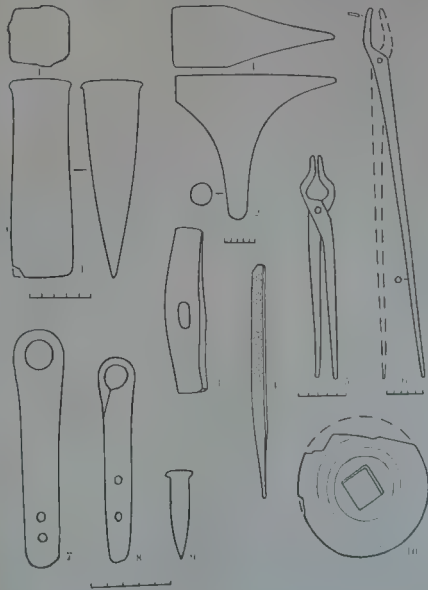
Инструменты кузнеца: 1 — наковальня из Витебска (Нижний замок); 2 — наковальня из Райковецкого городища (УССР); 3—5 — молоток, напильник и клещи из Дружки; 6—10 — клещи, гвоздильни, борода и точильный круг из Минска
